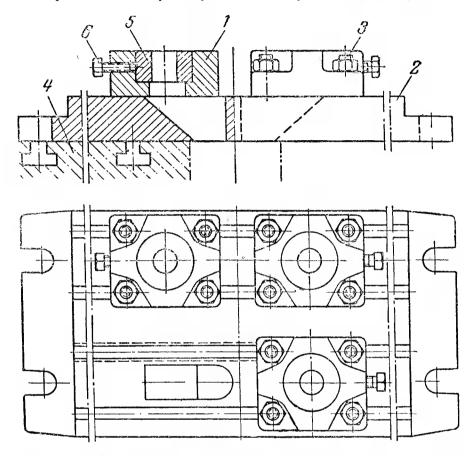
Групповое крепление матрицедержателей при двухрядной штамповке.
